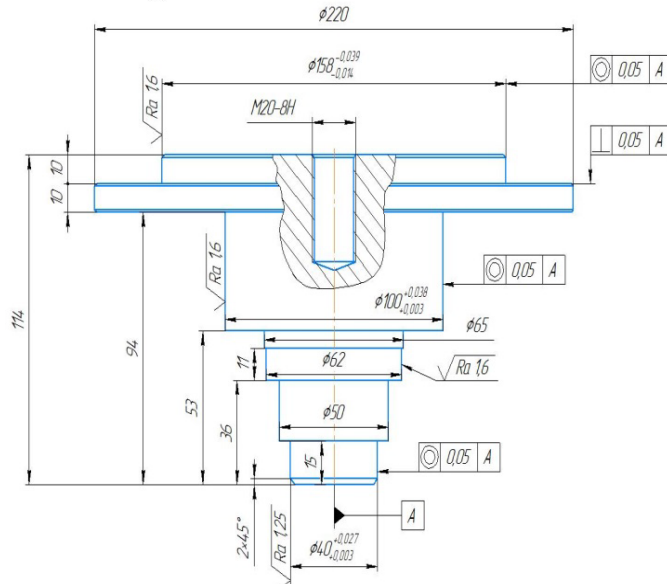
Многоступенчатая цилиндрическая оправка для контроля детали «Крышка насоса»
